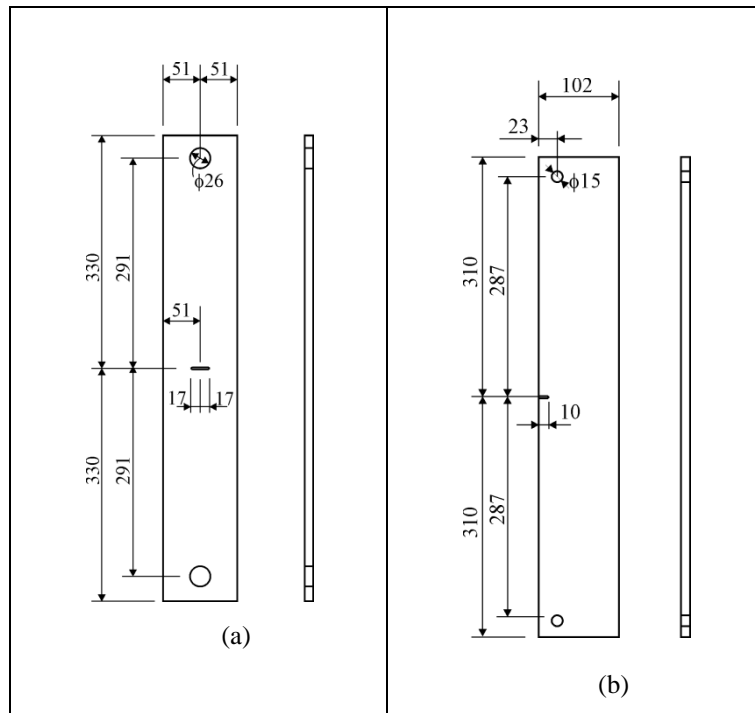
Geometria dos CPs com dimensões em milímetros: (a) um entalhe central e (b) um entalhe de borda.
